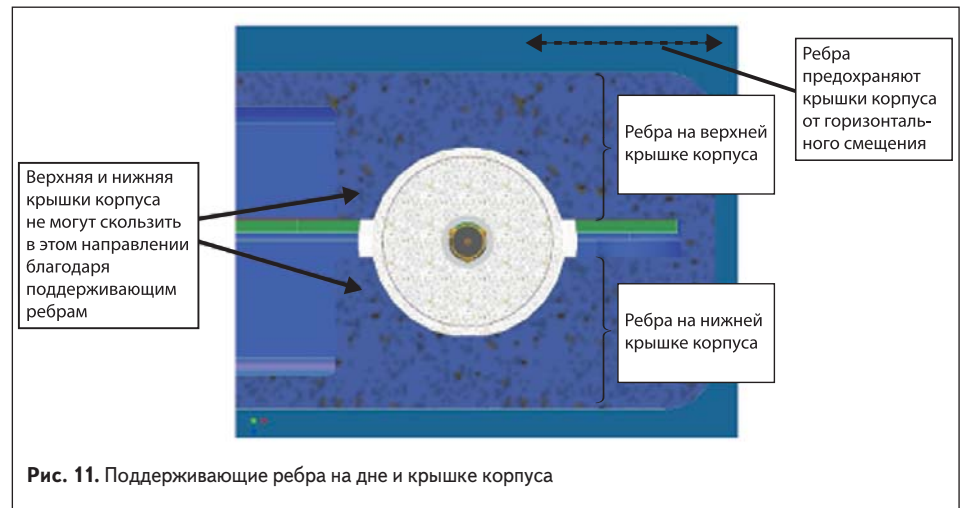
Поддерживающие ребра на дне и крышке корпуса
